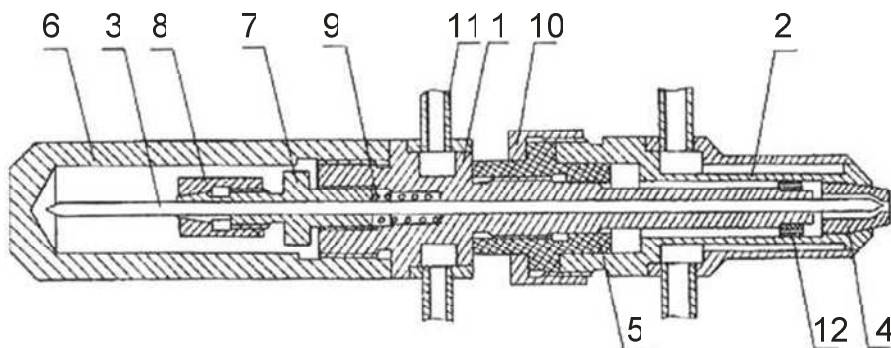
Общий вид плазмотрона для сварки тонкостенных труб:
